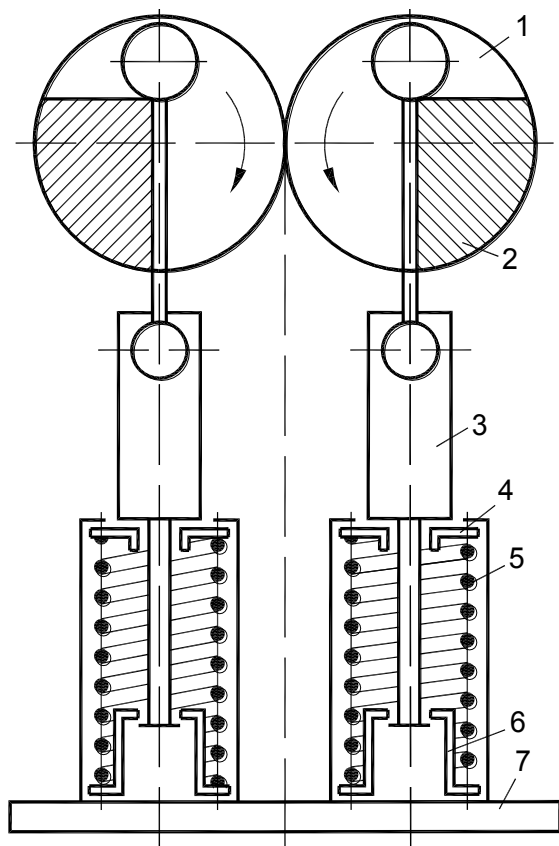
Схема механизма привода ручной трамбовки
